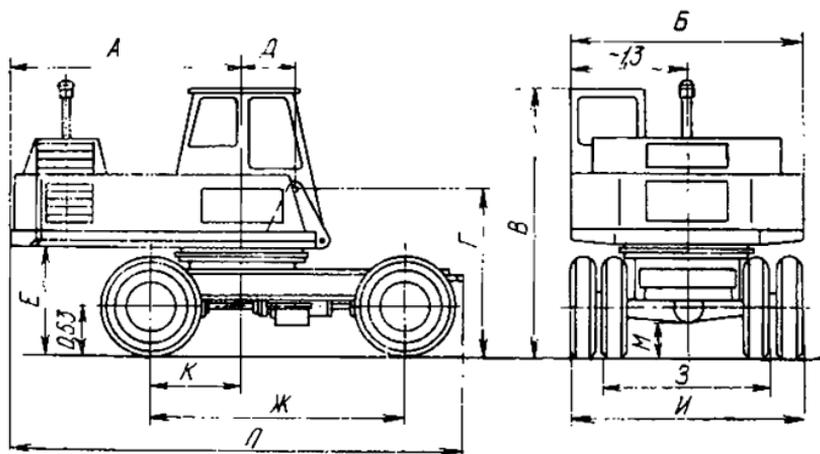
Габаритные размеры пневмоколесных полноповоротных экскаваторов
